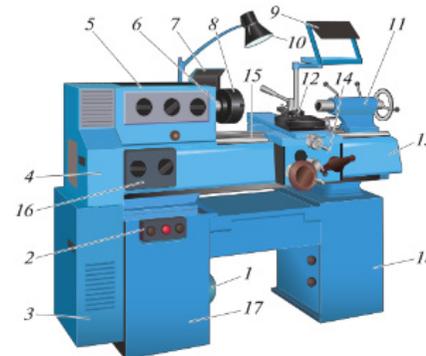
Токарно-винторезный станок ТВ-6: 1 — электродвигатель; 2 — кнопочная станция; 3, 4 — защитные кожухи; 5 — передняя бабка (коробка скоростей); 6 — шпиндель; 7 — откидной защитный кожух; 8 — трёхкулачковый патрон; 9 — откидной защитный экран; 10 — местное освещение; 11 — задняя бабка; 12 — суппорт; 13 — защитный кожух ходового винта и вала; 14 — фартук; 15 — станина; 16 — коробка подач; 17 — левая тумба; 18 — правая тумба
